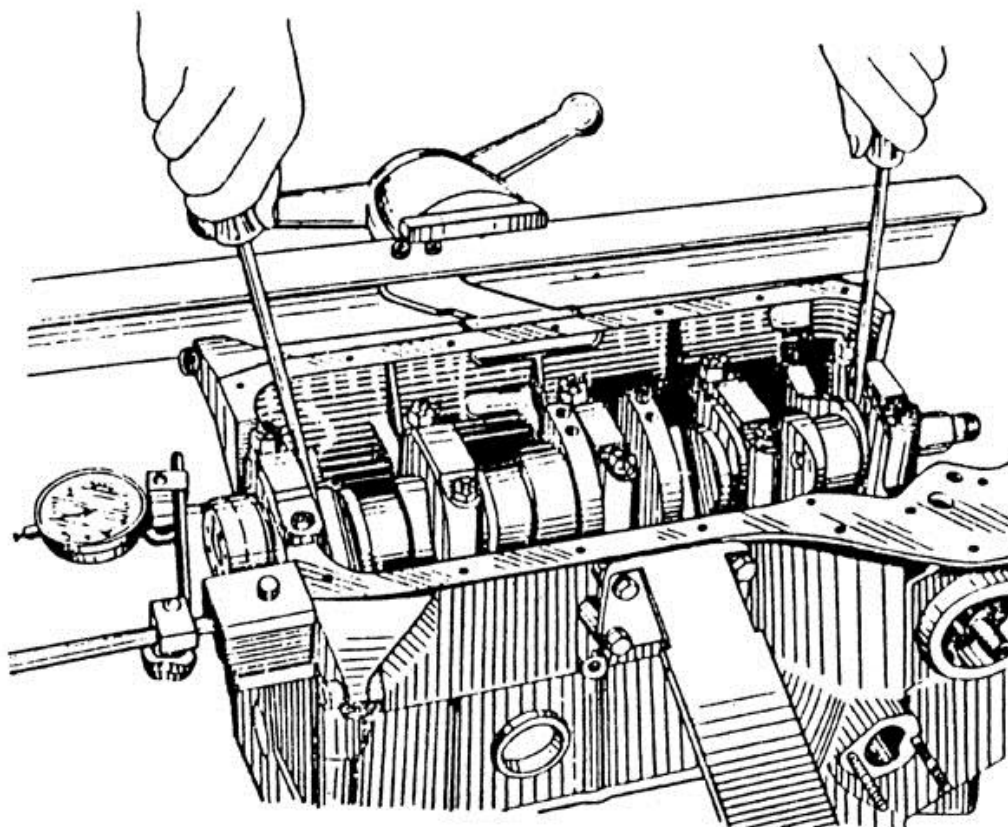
Проверка осевого зазора коленчатого вала
